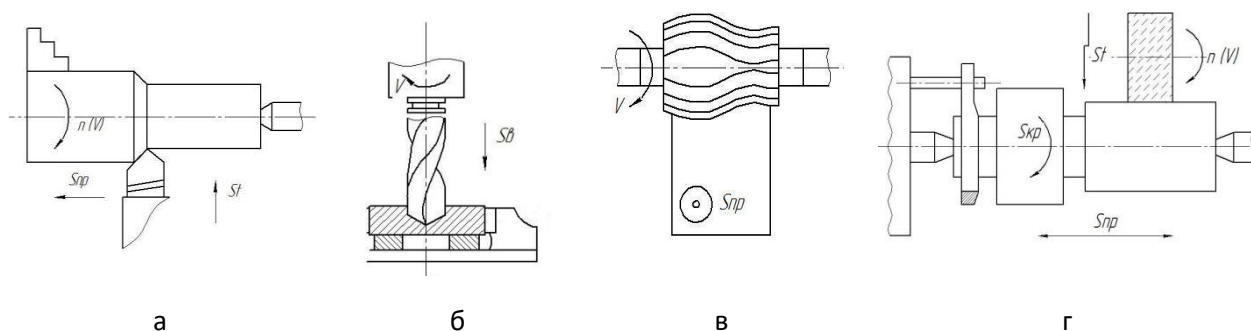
Схеми обробки заготовок гострінням (а), свердлінням (б), фрезеруванням (в), шліфуванням (г):
